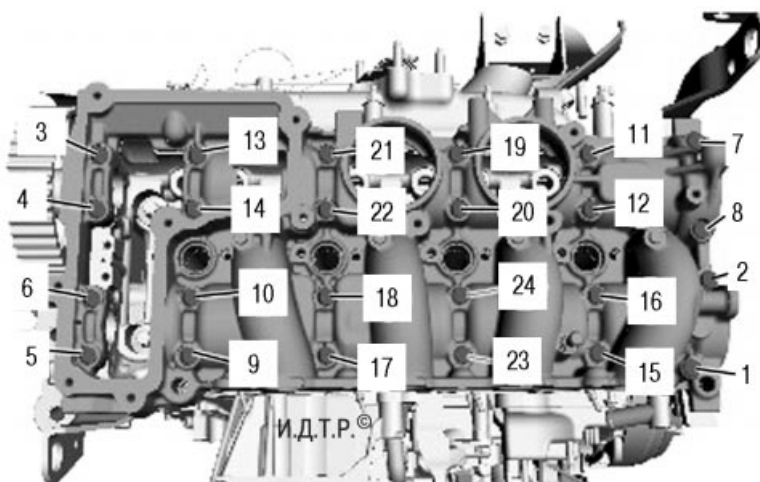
Порядок ослабления затяжки болтов крепления нижней части крышки головки блока цилиндров
